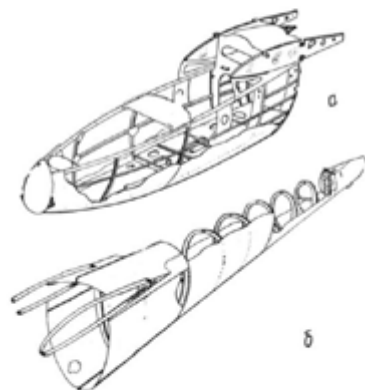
Конструкция фюзеляжа планера «Блазник»: а — передняя часть фюзеляжа выполнена по лонжеронной схеме; б — задняя часть фюзеляжа выполнена по монококовой схеме
